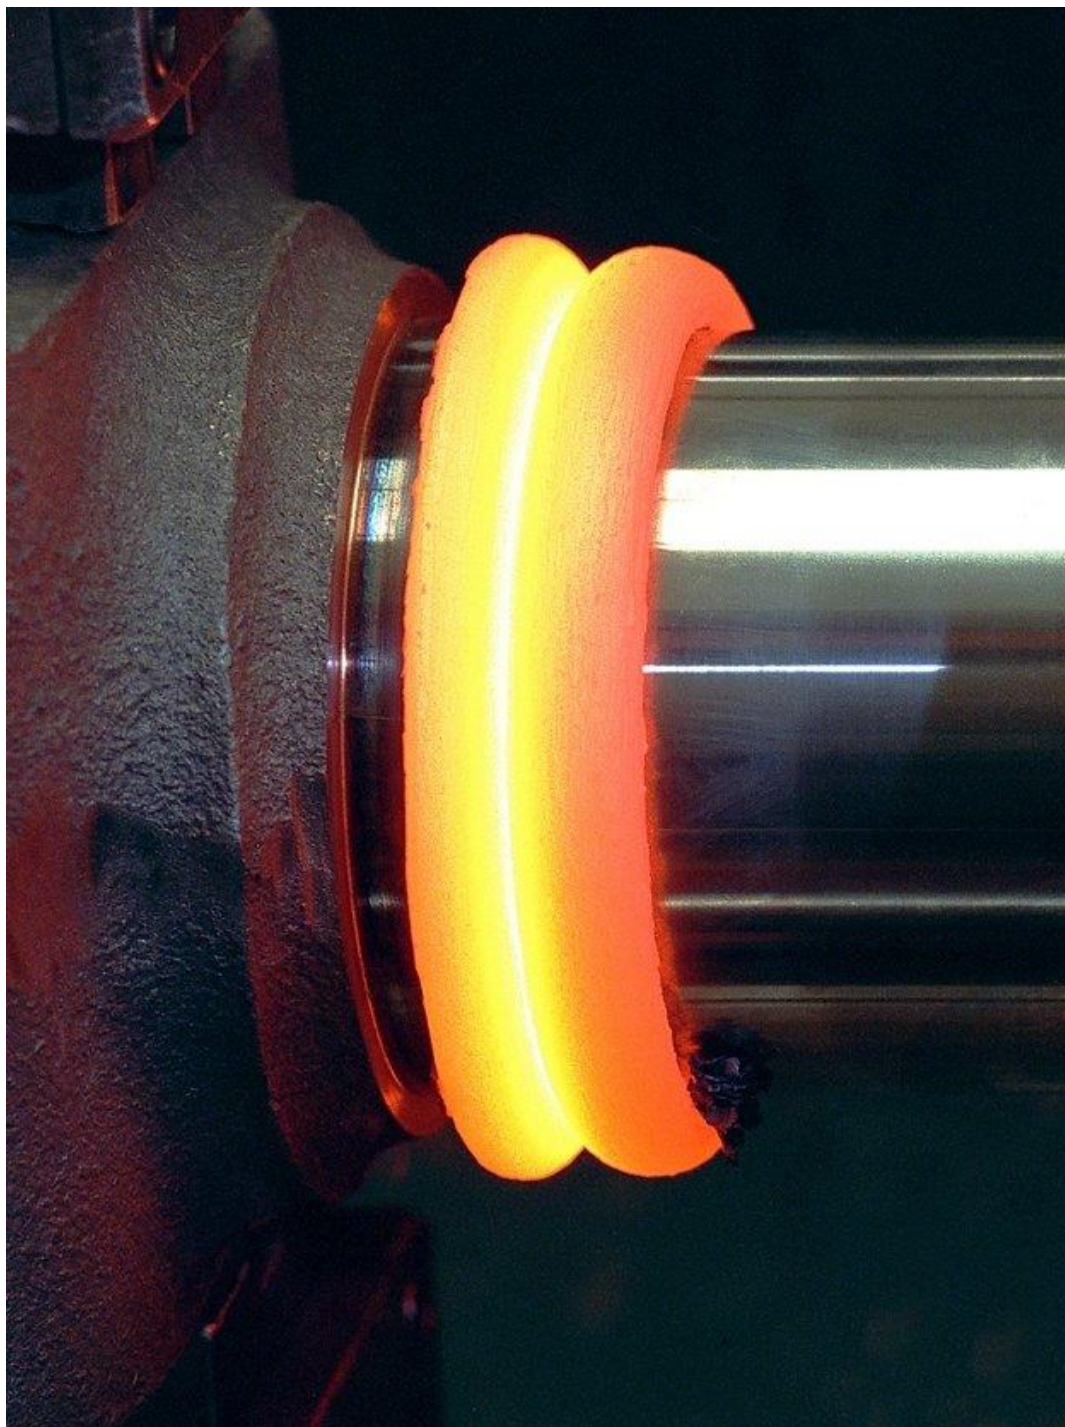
Общий вид соединения получаемого сваркой трением
